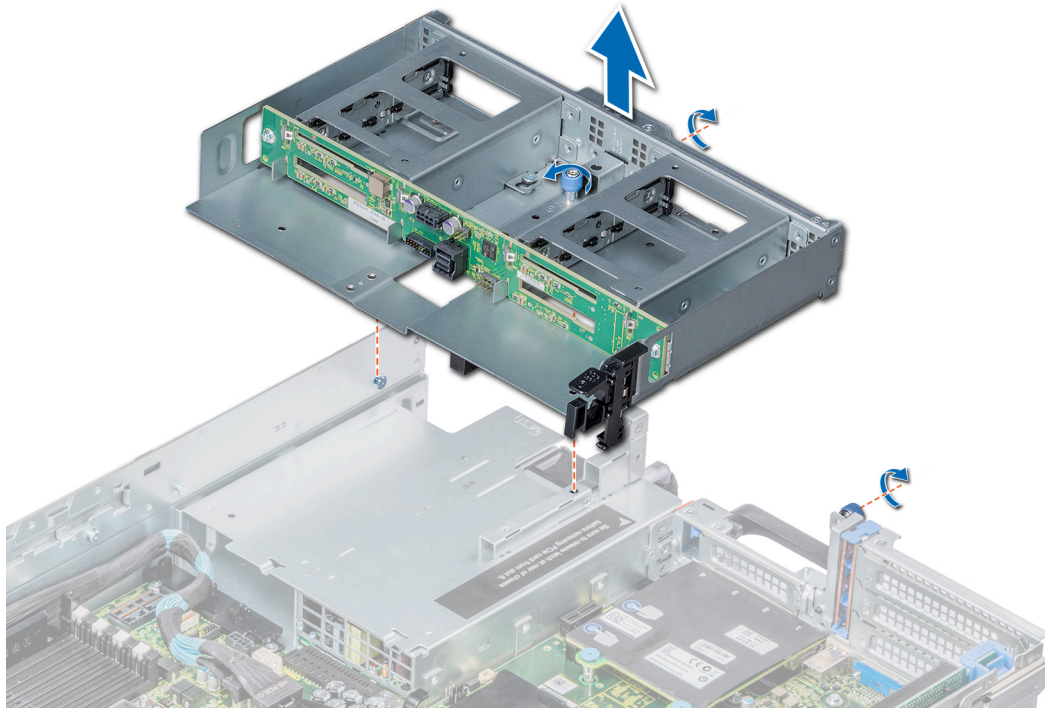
Entfernen eines hinteren Gehäuses mit vier 2,5-Zoll-Festplatten
